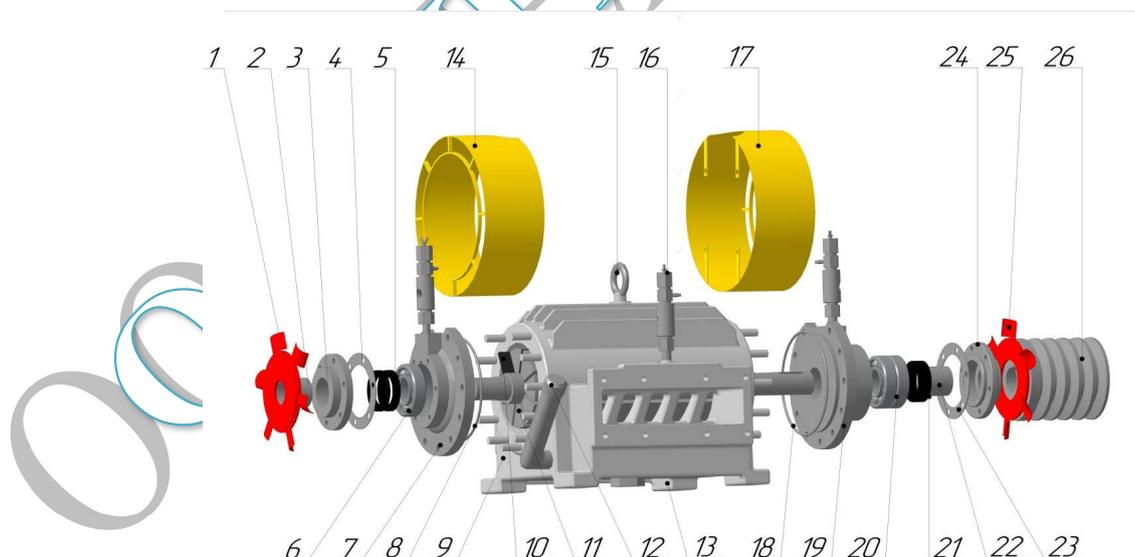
1,25 – крыльчатка; 2 – втулка задняя; 3 – малая крышка задняя; 4,23 – паронитовая прокладка; 5, 21 – манжета армированная; 6 – подшипник задний; 7 – крышка задняя; 8,18 – кольцо уплотнительное; 9 – корпус; 10 – пластина; 11 – ротор; 12 – заливная горловина; 13 – сливная пробка; 14,17 - защитный кожух крыльчатки; 15 – рым болт; 16 – капельница; 19 – крышка передняя; 20 – подшипник передний 2 шт; 22 – втулка передняя; 24 – малая крышка передняя; 26 – шкив.
